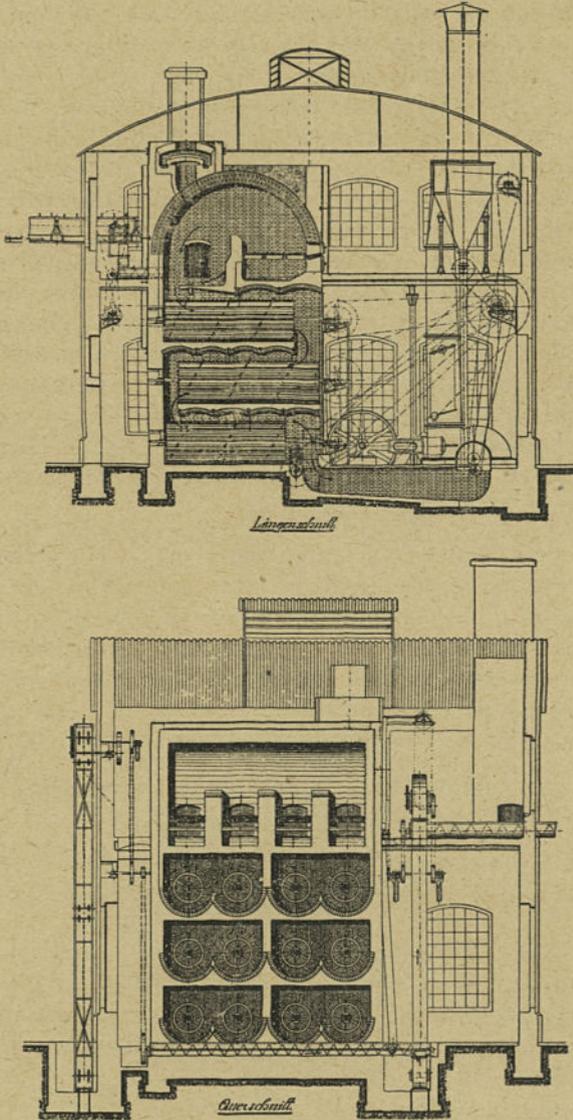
Coupe longitudinale et coupe transversale d'un four Böttner et Mayer.
